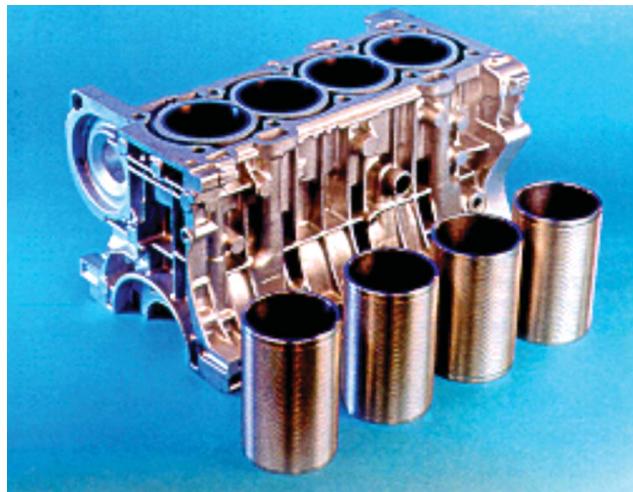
Рядный 4-цилиндровый алюминиевый блок двигателя Volvo с втулками из чугуна
